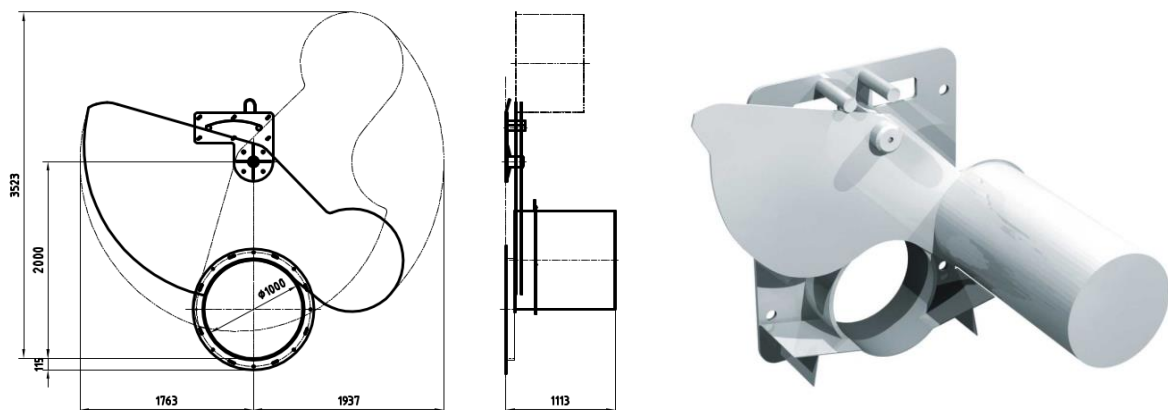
Abflussregler mit Schwimmsteuerung; HydroSlide Bauart Mini - Steinhardt Wassertechnik [U6]
